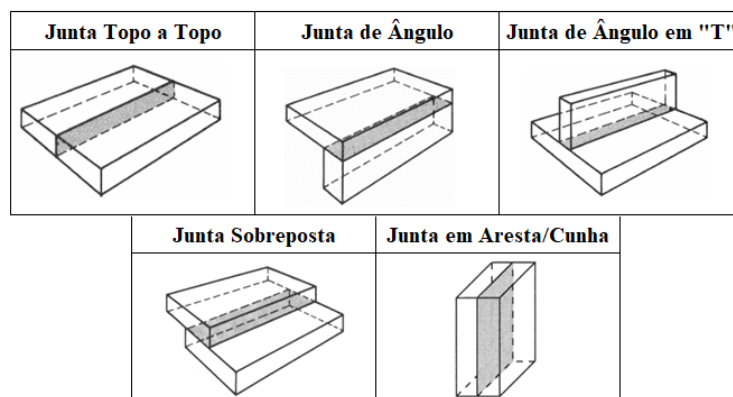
Tipos de juntas de soldadura segundo EN ISO 9692 [14]
